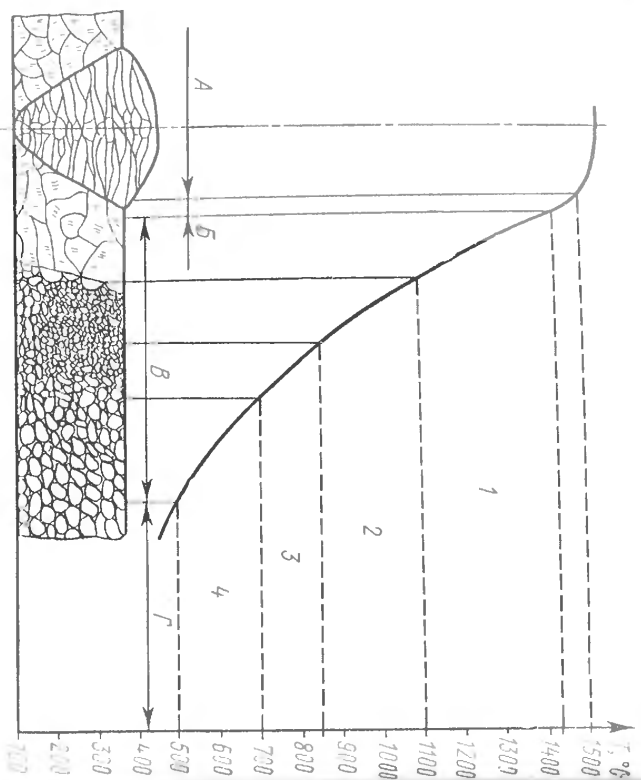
Схема строения сварного соединения при дуговой сварке стали:
